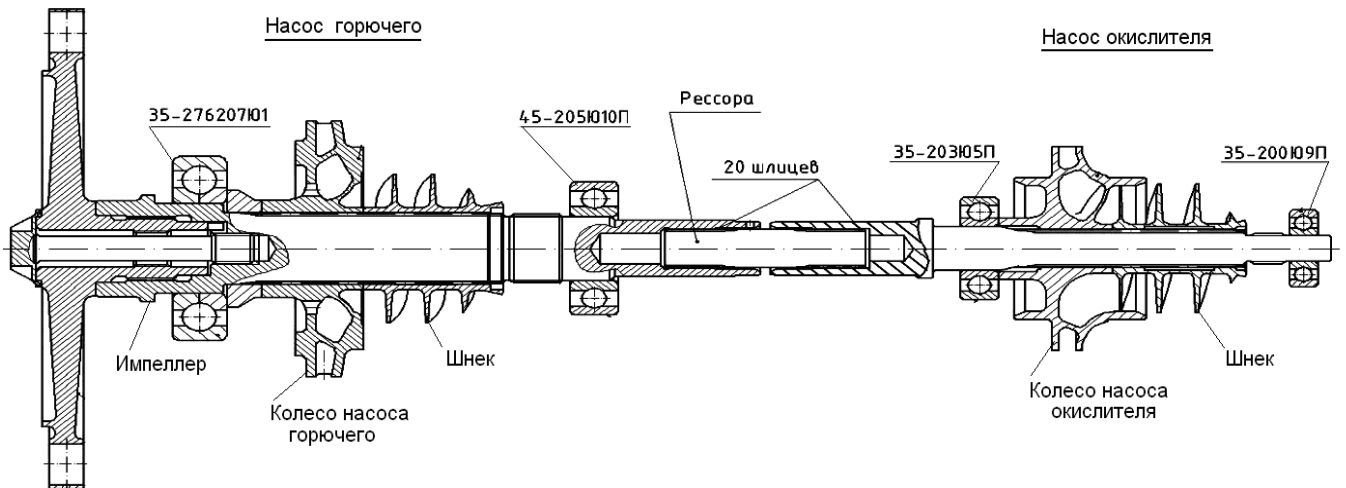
Конструктивна схема ротора ТНА з опорами
